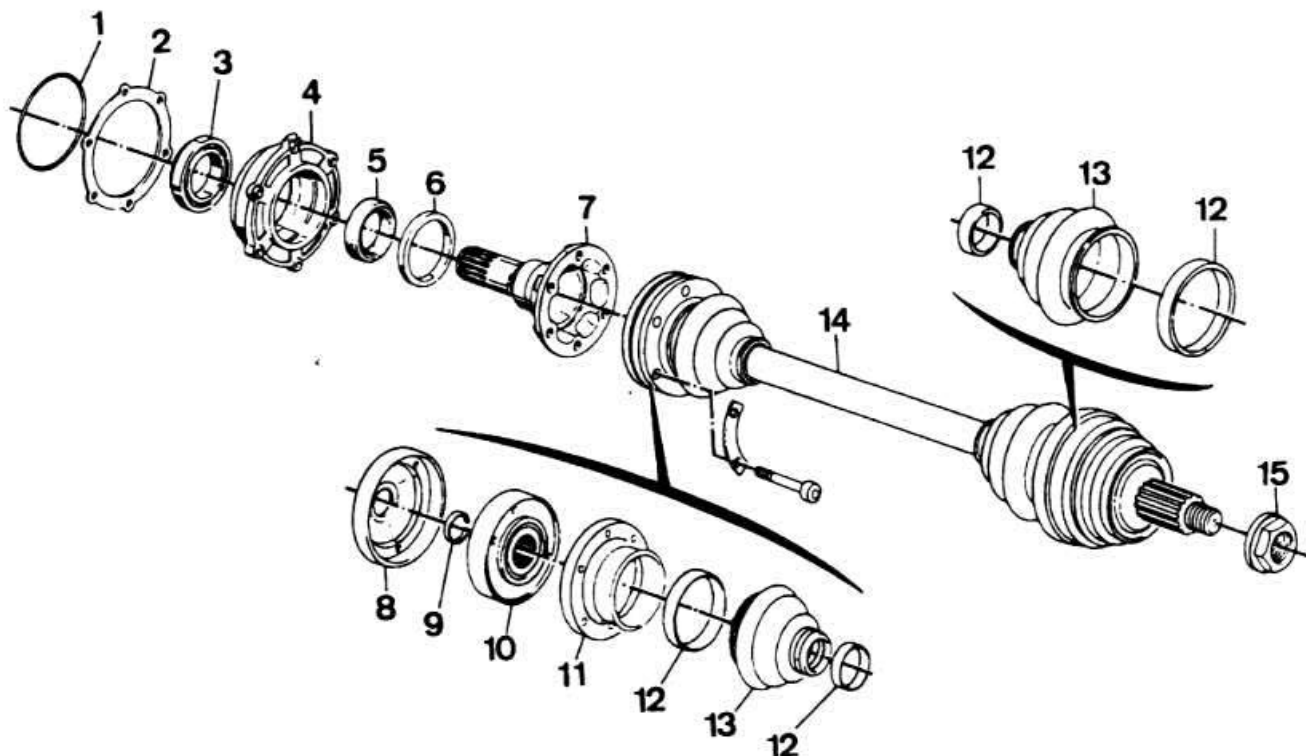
Детали вала привода заднего колеса автомобилей с бензиновыми двигателями:
